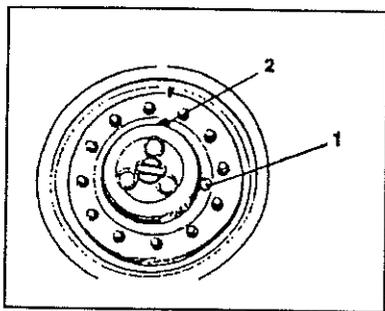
Engranaje planetario/posición de llenado de aceite
